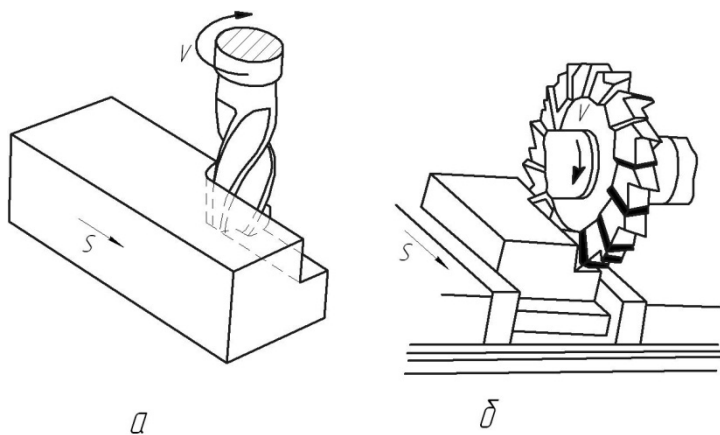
Схемы фрезерования уступов Рисунок 3.4 — Фрезерование уступов
